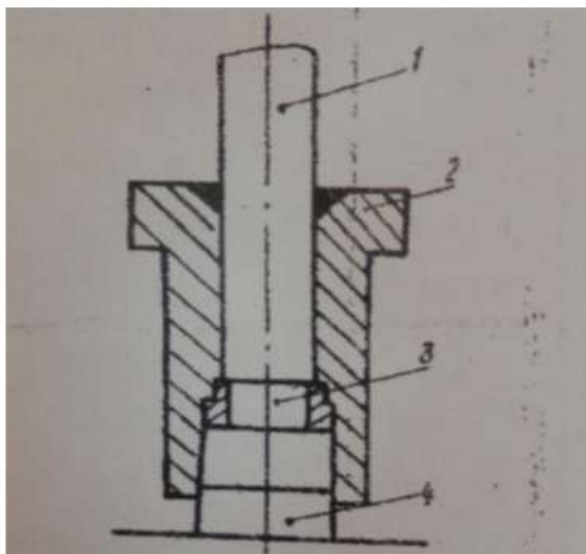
Устройство для запрессовки пека в кольцо: 1 – поршень; 2 – направляющая втулка; 3 – кольцо; 4- пробка
